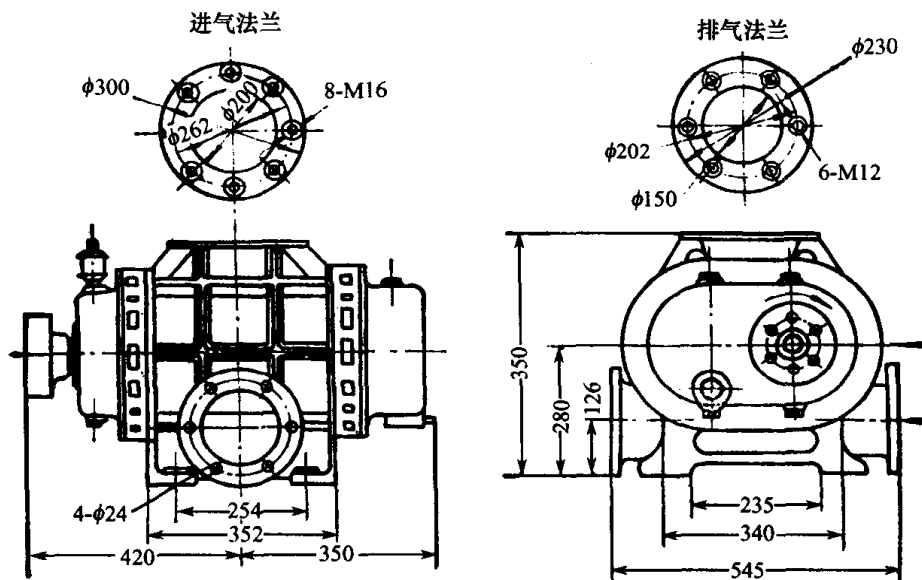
ZJ-600C 型罗茨泵外形及安装尺寸
